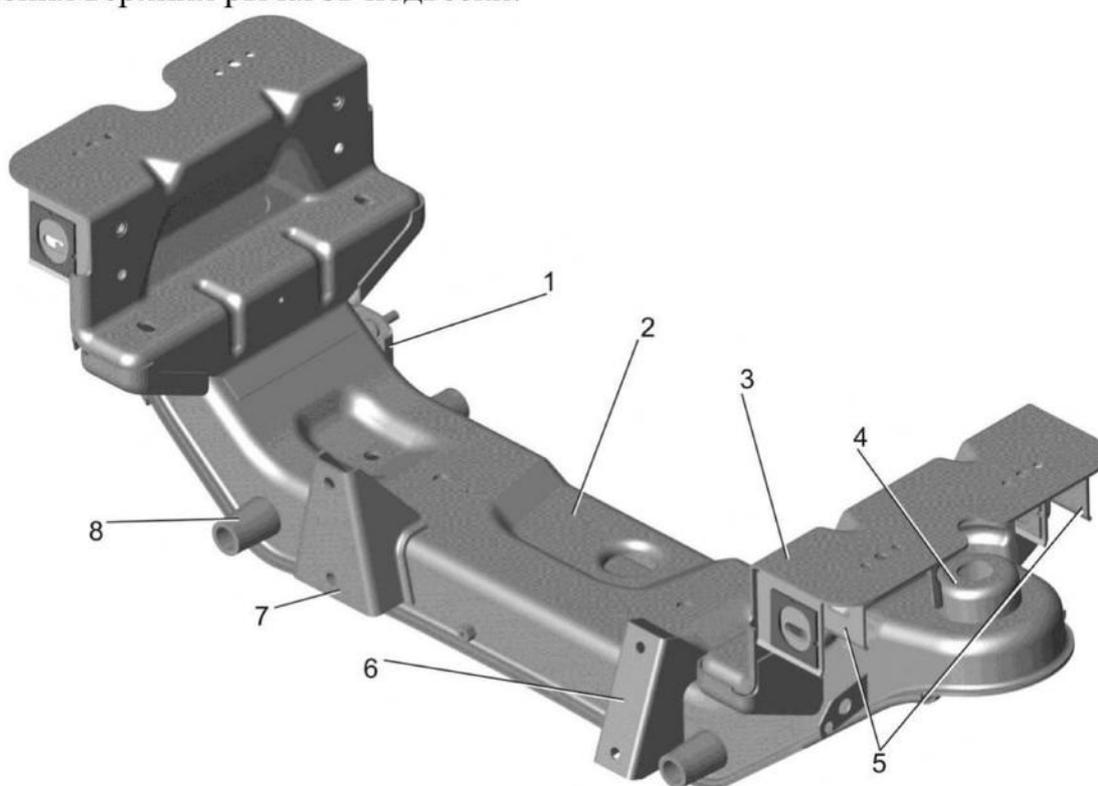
Подрамник: 1- кронштейны крепления штанги стабилизатора; 2- поперечина; 3 - кронштейны крепления поперечины; 4- чашки амортизаторов; 5- кронштейны крепления верхних рычагов; 6,7 – правый и левый кронштейны крепления рулевого механизма; 8 - втулки осей нижних рычагов
